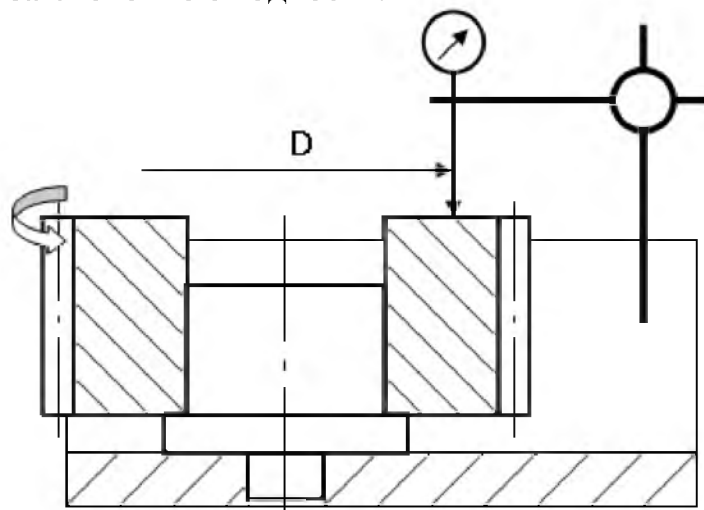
Схема измерения торцевого биения зубчатого колеса
